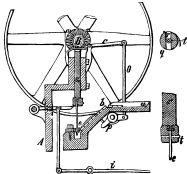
Durchschn. Fig. 3. Fig. 4. Rod's Schraubenmutter-Schneidmaschine.
